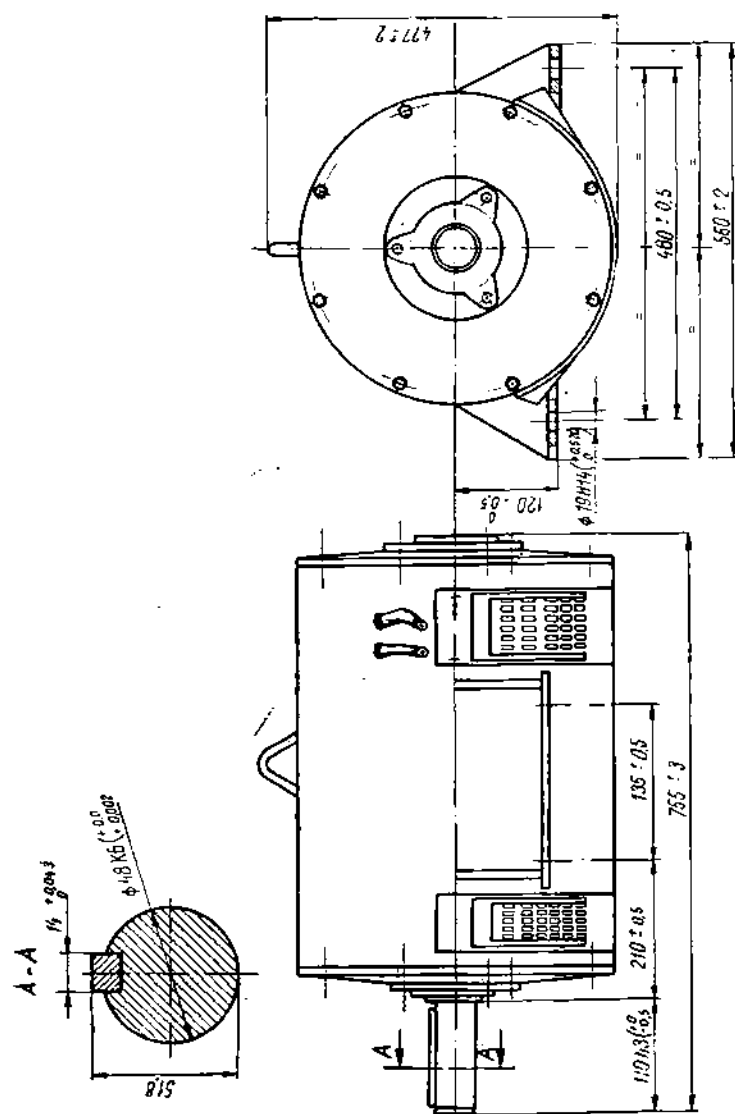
Motor tip Ce 225 — 5,5 kW. Dimensiuni de montaj.
